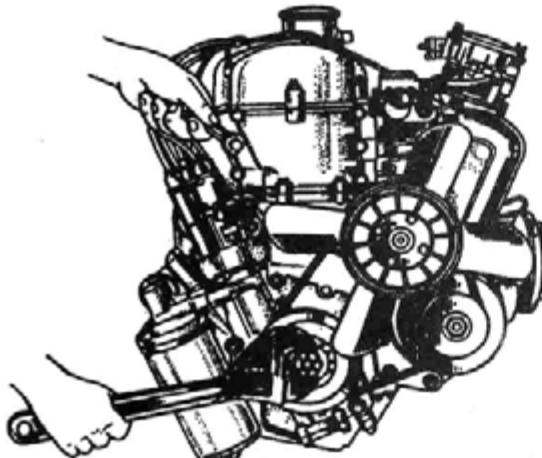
Затяжка стопорного болта натяжного устройства цепного привода газораспределения
